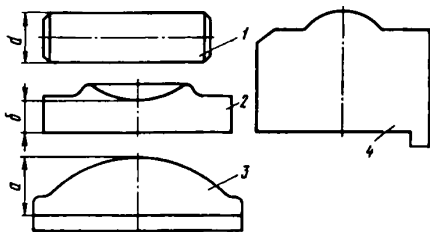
Детали упругого устройства автосцепки СА-3М
